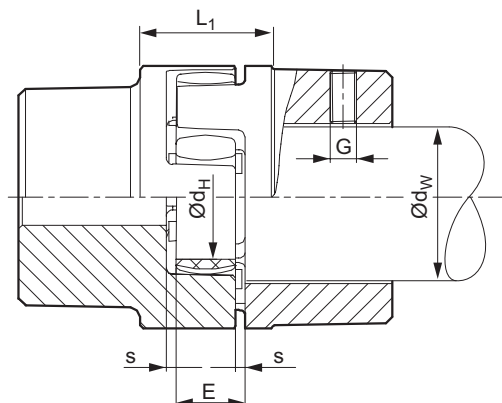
Dimensões de montagem do acoplamento ROTEX ^{51689AXX}
